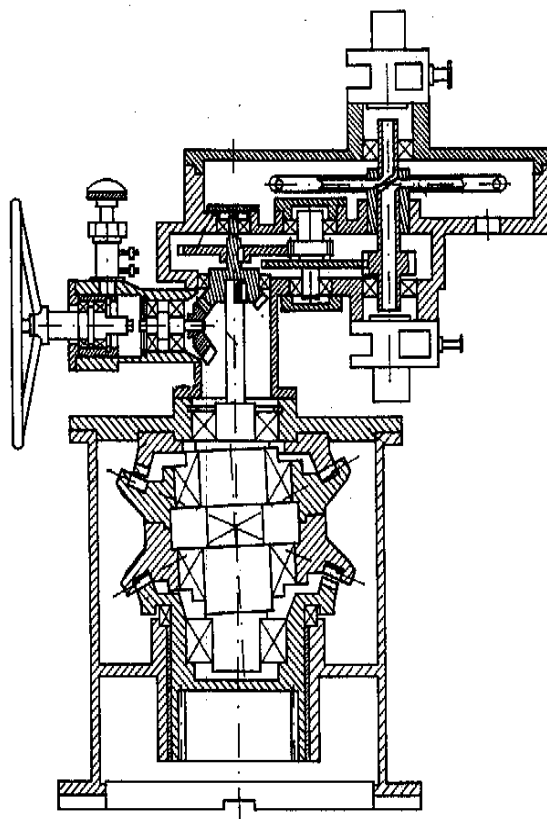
Струминно-реактивний двигун з прецесійним редуктором
